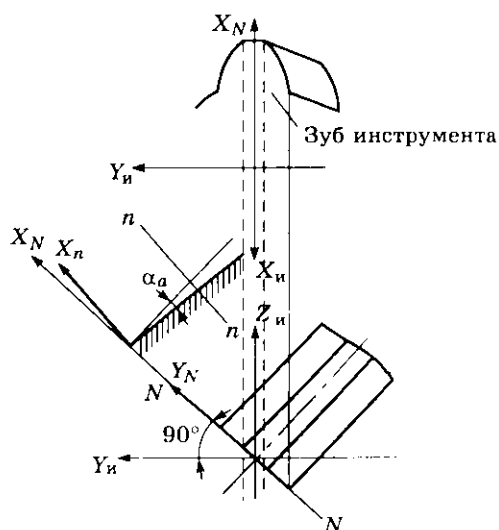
Схема к расчету координат точек профиля зуба обкаточного резца
